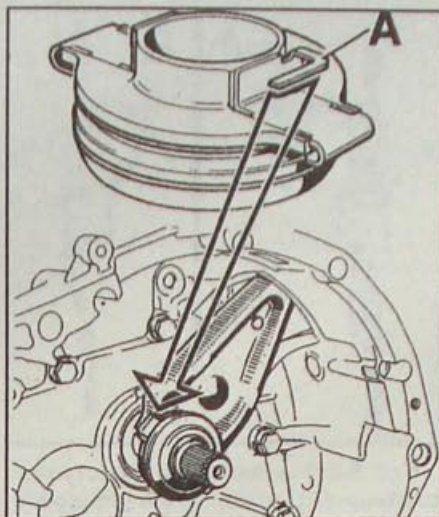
Установка подшипника выключения сцепления на направляющую втулку:
